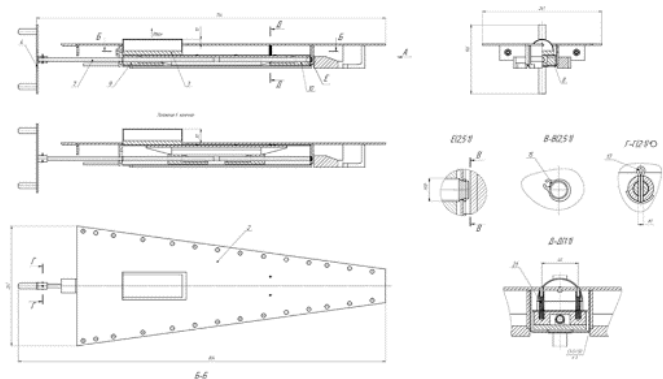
Сборочный чертеж приемного диверторного устройства с подвижным модулем
